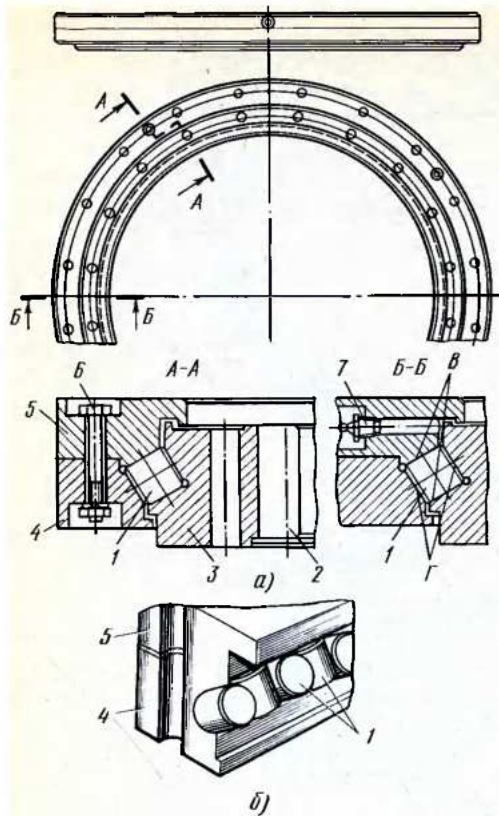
Нормализованное роликовое опорно-поворотное устройство с внутренним зубчатым венцом:
